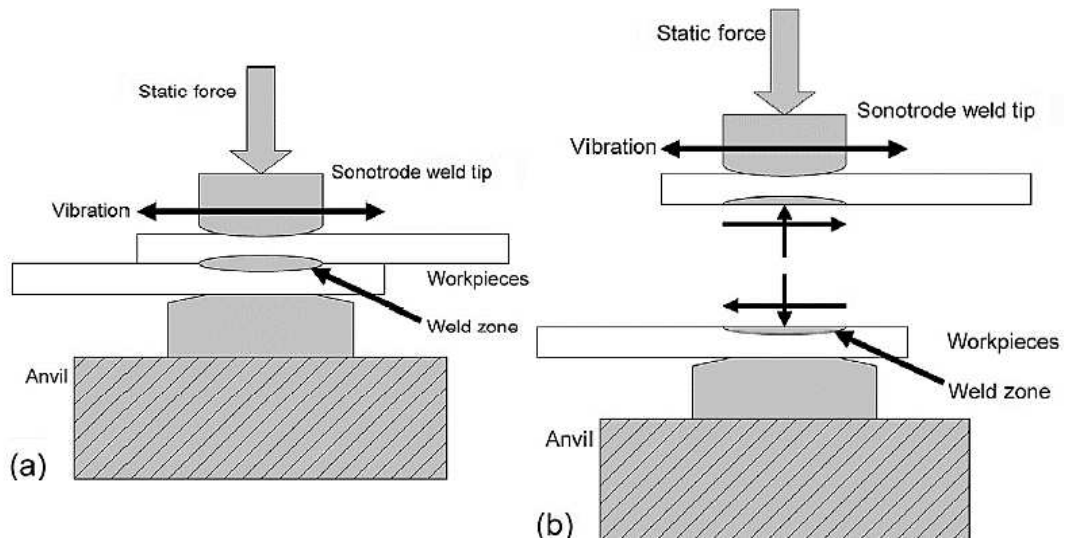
Схема УЗС: (а) знакопеременные тангенциальные смещения, сообщаемые заготовкам и зоне сварки, и (б) нормальные силы и силы сдвига, действующие на зону сварки [31]
